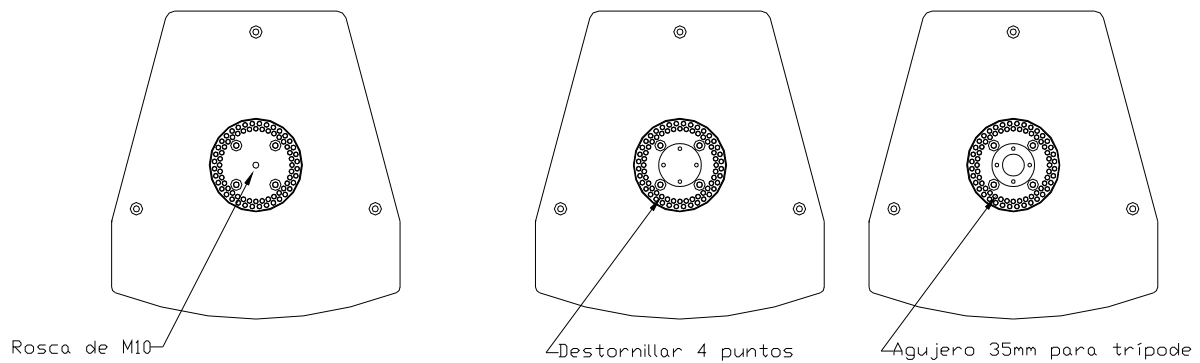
Parte superior (izquierda) y parte inferior (derecha)
